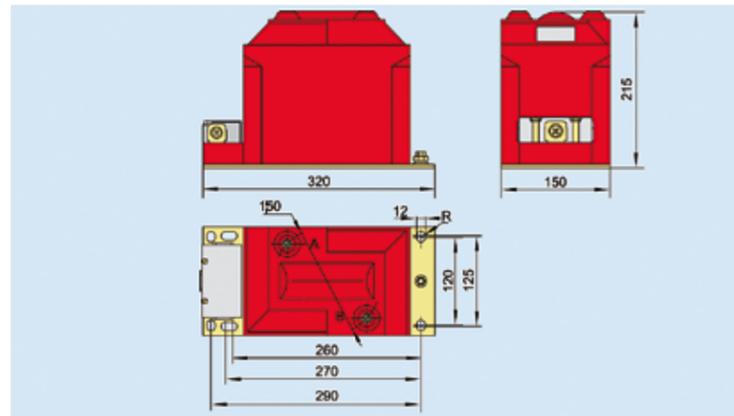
Внешний вид и размеры трансформатора напряжения JDZ10-10
